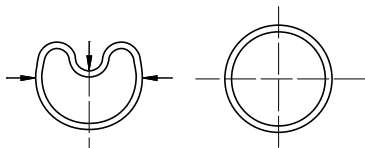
Slipper Seal®, уплотнение штока, установка 2
